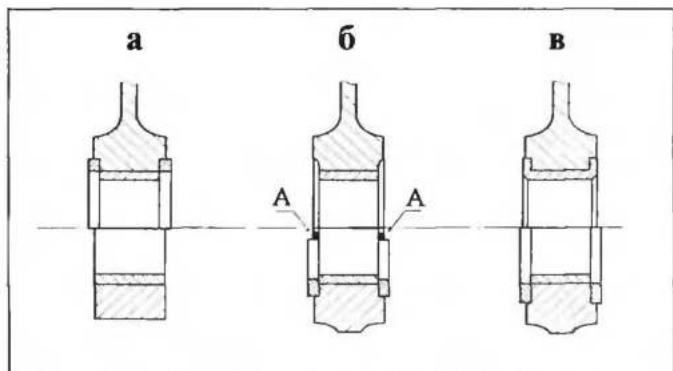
Некоторые способы ремонта упорных поверхностей на блоке цилиндров:
